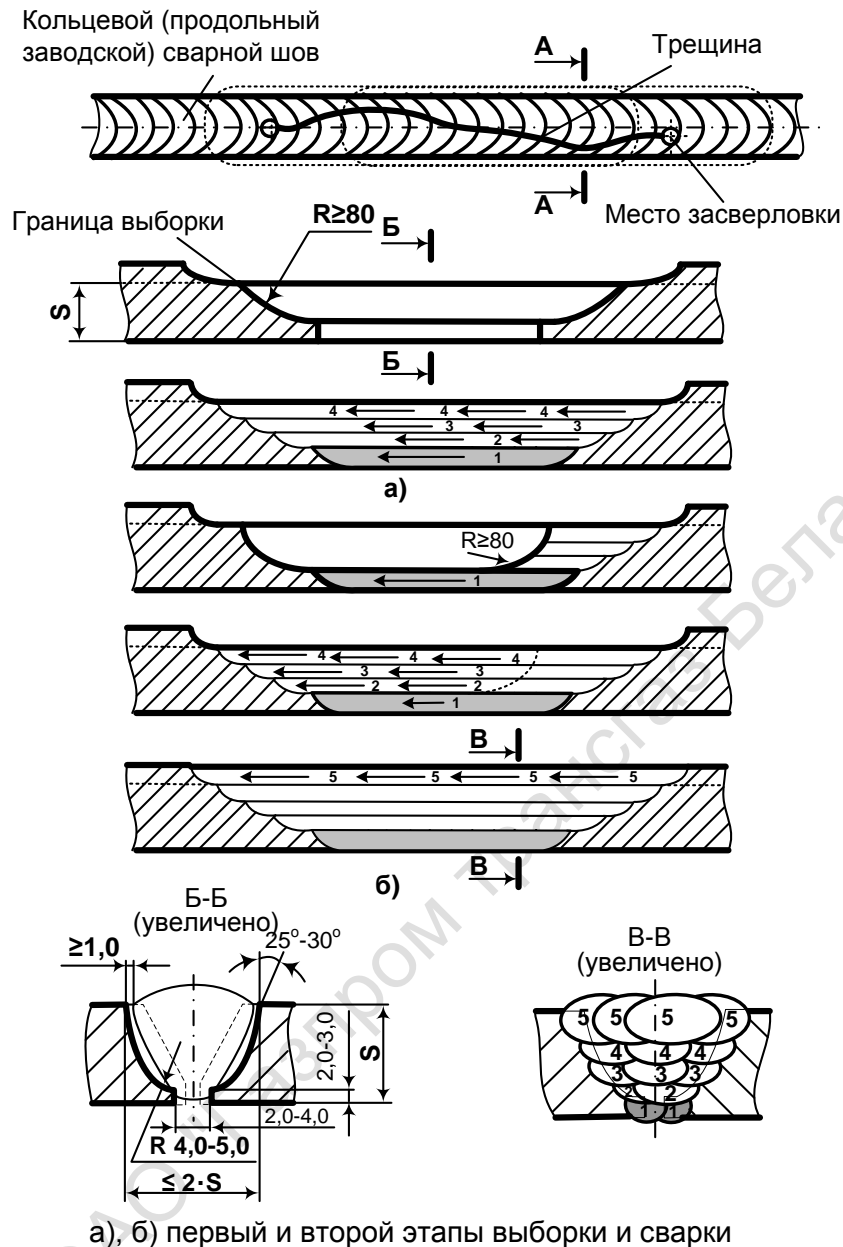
Параметры выборки дефектного участка, последовательность и направление слоев шва, параметры сварного шва при сварке (заварке) сквозной выборки прямолинейной формы длиной до 250мм
